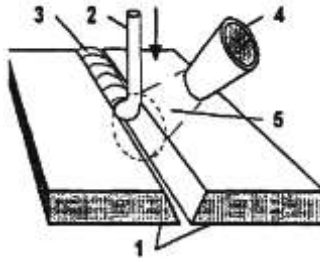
Зварювання пластмас: 1 – зварювальні деталі; 2 – присадний матеріал; 3 – зварний шов; 4 – насадка нагрівача; 5 – струмінь нагрітого стиснутого повітря
